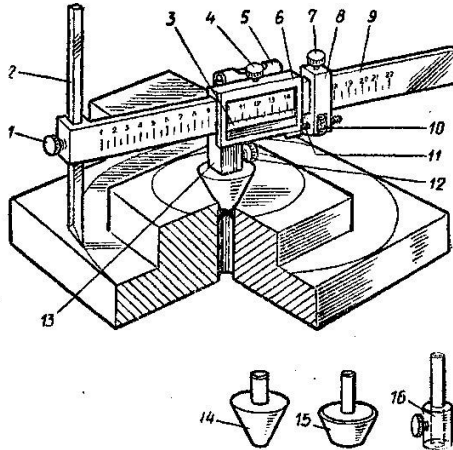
Вдосконалений розмічальний штангенциркуль для кіл великих діаметрів: 1 – стопорний затискач; 2 – різець; 3 – ноніус; 4, 12 – затискачі; 5 – рівень; 6 – рамка; 7 – гвинт; 8 – хомутик; 9 – штанга; 10 – гайка; 11 – мікрометричний гвинт; 13 – вставка; 14, 15 – змінні опори; 16 – подовжувач
